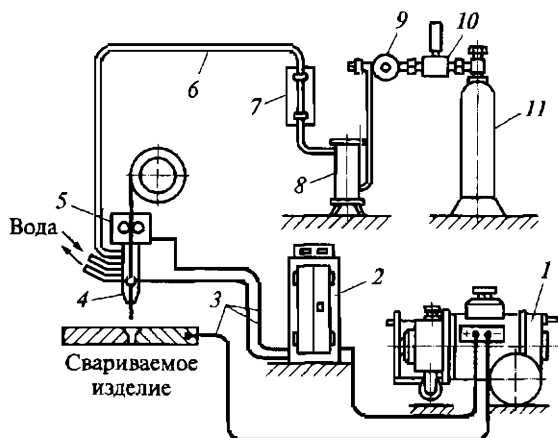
Пост полуавтоматической сварки электродом в среде защитного газа:
